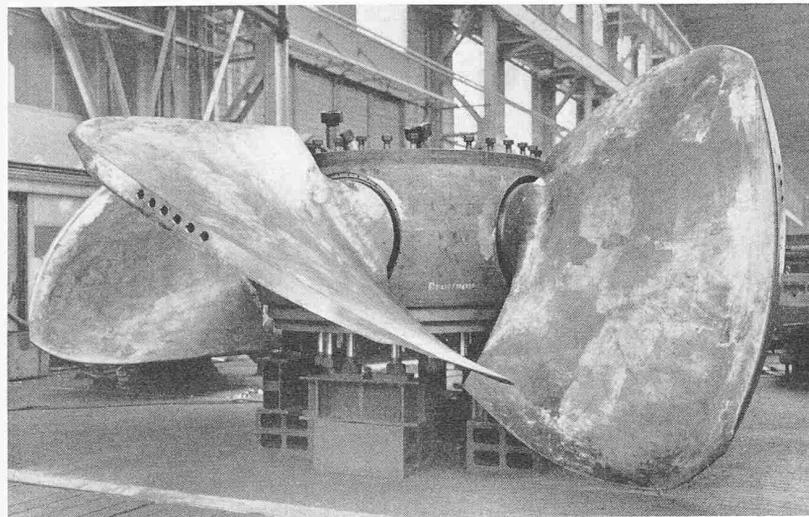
Turbinenrad, Schaufel rechts umgewendet
